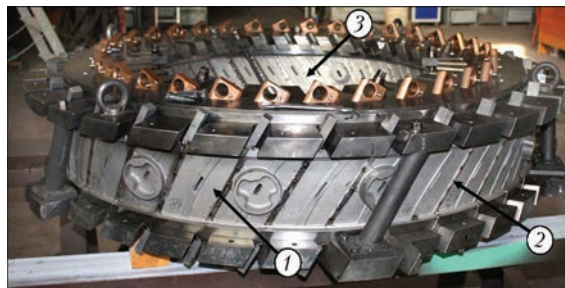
Внешний вид наружной части переднего корпуса КСД в сборочно-сварочном приспособлении: 1 — стойки; 2 — наружные стыки между стойками; 3 — внутренние стыки между стойками
